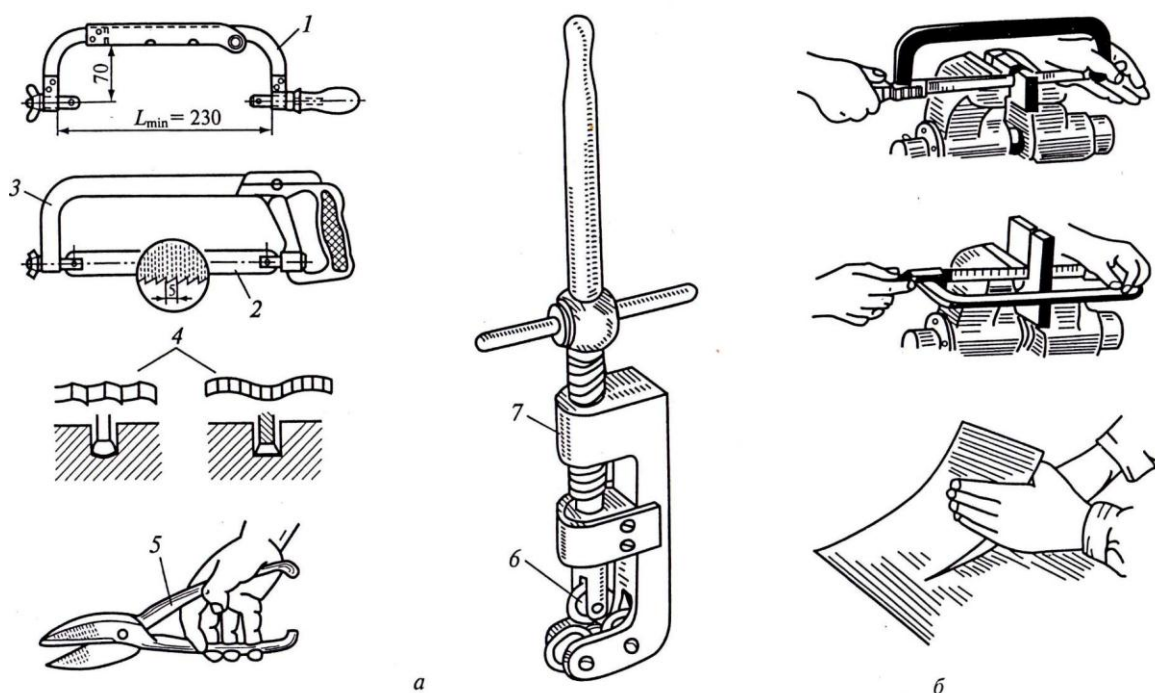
Ручне різання металу: *а* - ручний інструмент; *б* - прийоми різання; 1 – ножівка традиційної конструкції; 2 - ножівкове полотно; 3 – ножівка з вертикальною рукояткою; 4 – види розведення зубів пиляльного полотна; 5 – ножиці; 6 – відрізни ролики; 7 – роликовий труборіз
